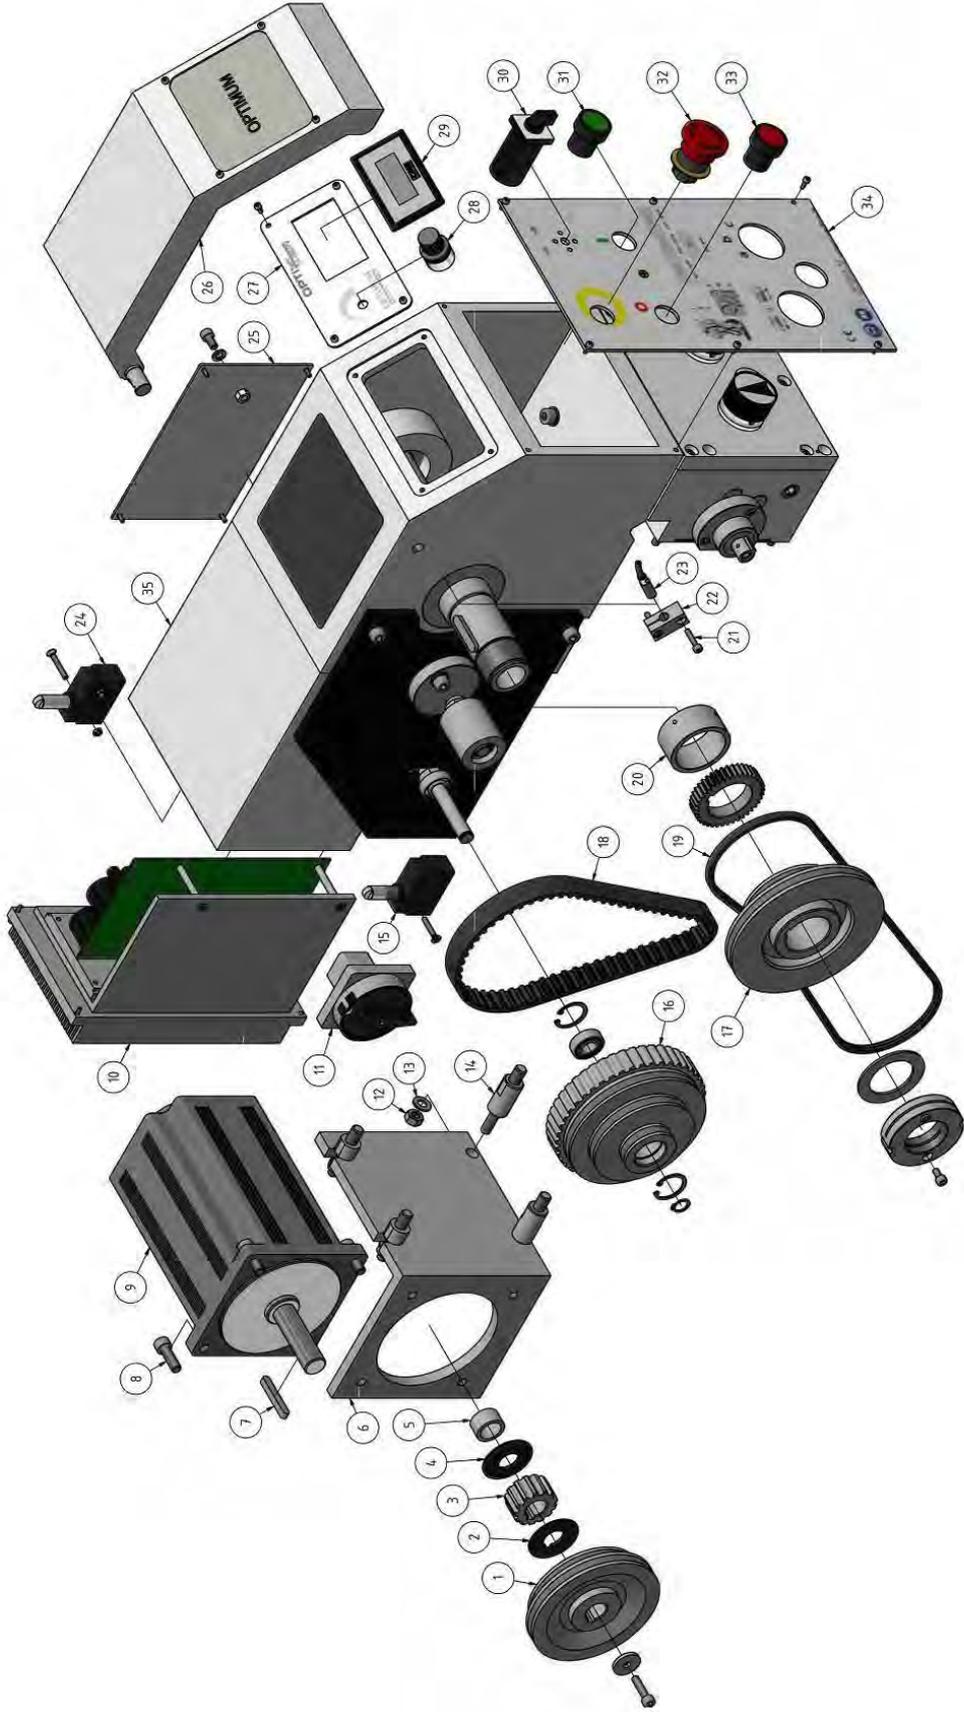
Spindelstock - Cabezal TU 2807 V
